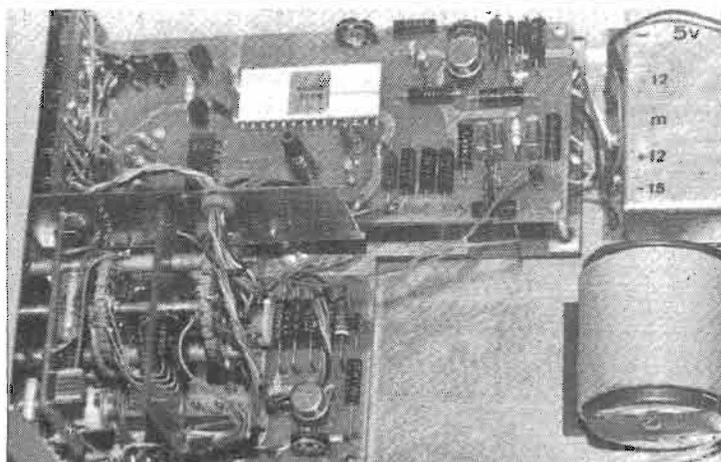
Le MX38 est terminé. On distingue le commutateur de gammes au premier plan.
